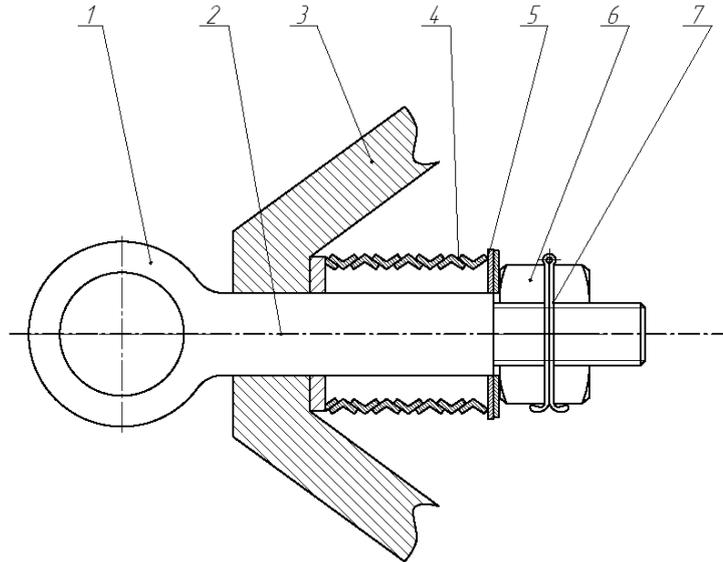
Схема предлагаемой конструкции сцепного устройства прицепа:
